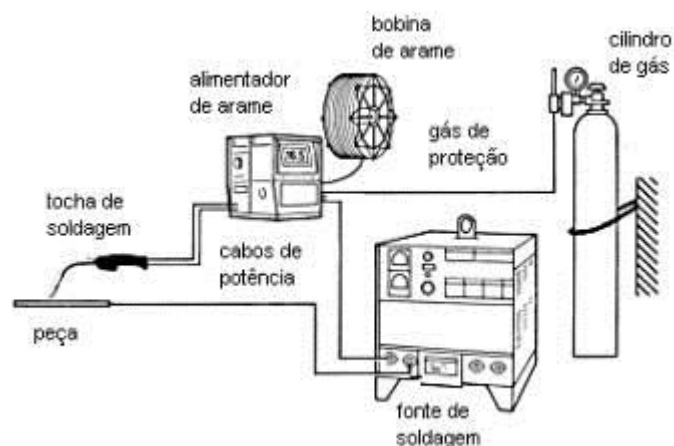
Componentes do processo de soldagem MIG/MAG [5]
